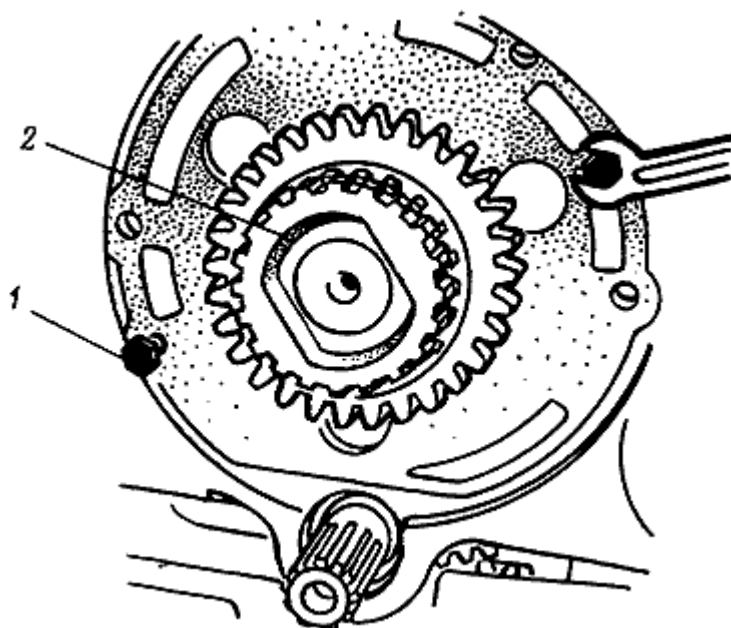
Выпрессовка вала сцепления и снятие ведущего диска тормозка:
